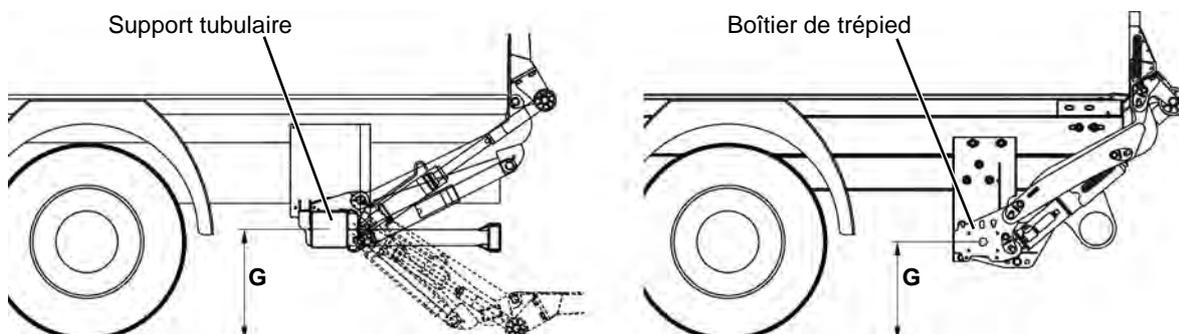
Distance entre le mécanisme de levage et le sol (dimension G)
